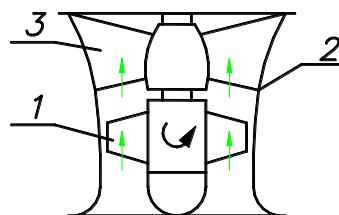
Схема осьового насоса: 1 – робоче колесо; 2 – корпус; 3 – випрямний апарат
